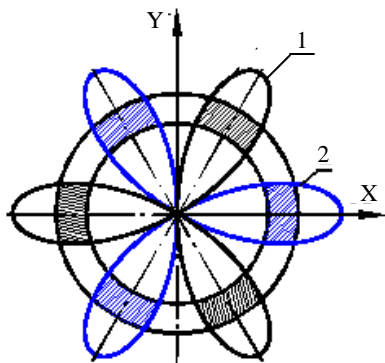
Схема формирования траектории исполнительного движения при дискретно-непрерывном движении деления:
